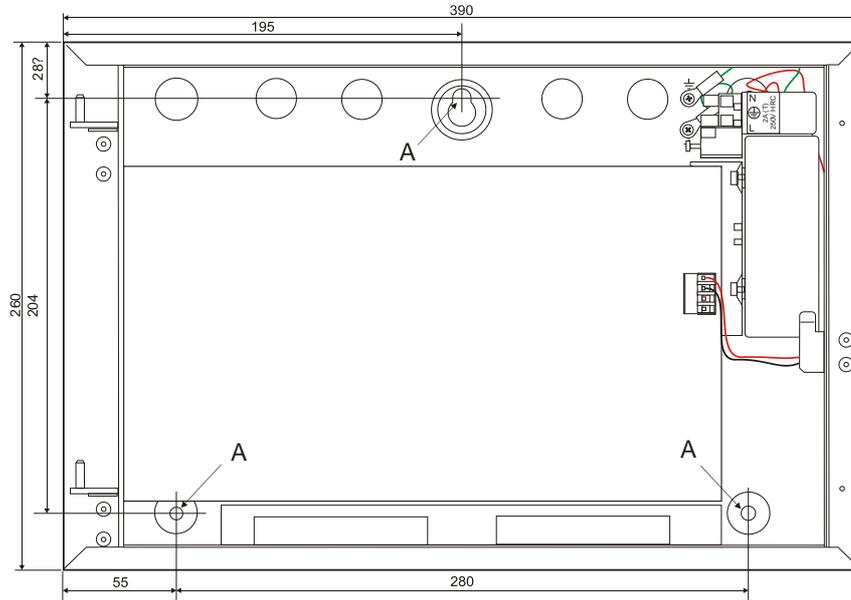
Dimensões e pontos de fixação - caixa pequena
